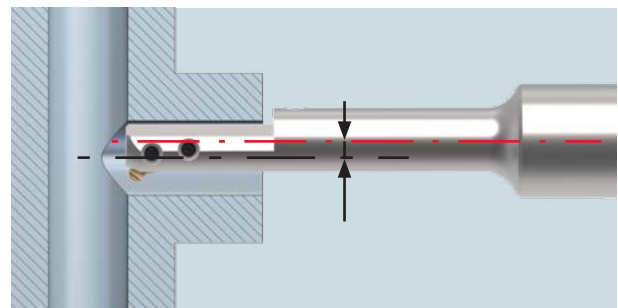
Die Entgratung des T-Stücks erfolgt durch die Querbohrung.
